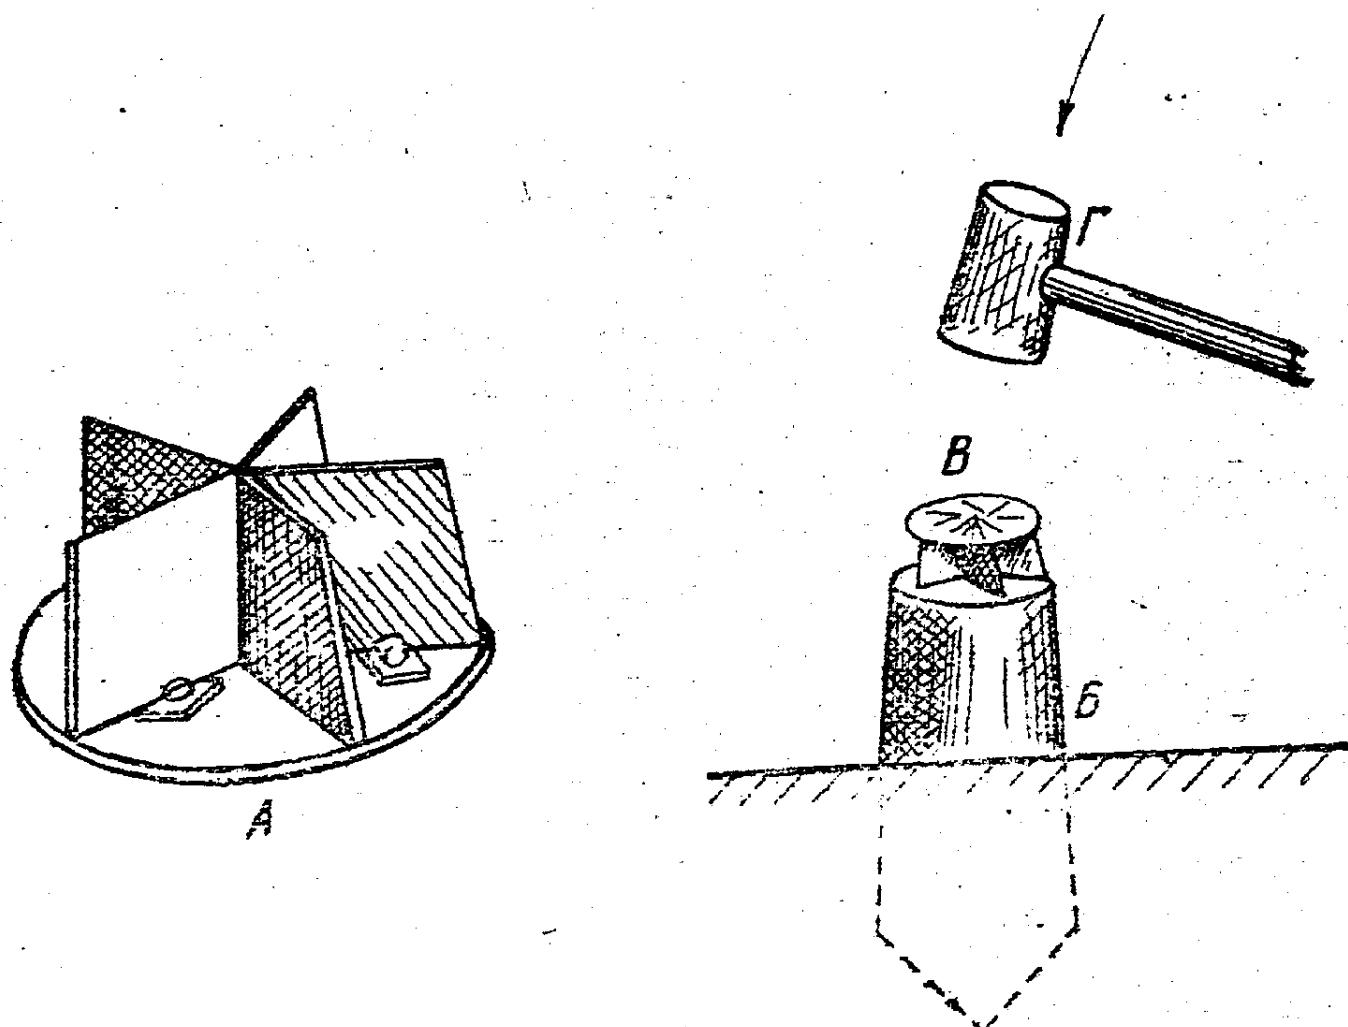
Колун В. А. Виноградова. А — чугунная пластина с пятью ножами; Б — подставка-наковальня с пластиной; В — раскалываемая плашка; Г — деревянный молот.
